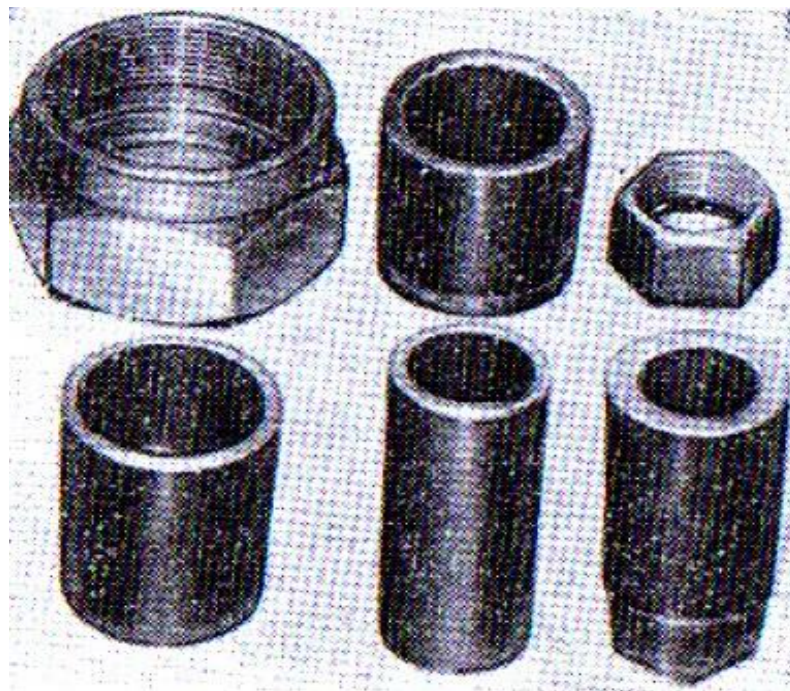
Деталі, заготовки яких отримані зворотним способом
